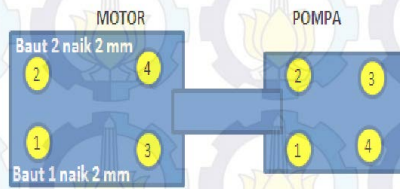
Posisi baut pada prototype base pompa dan motor
